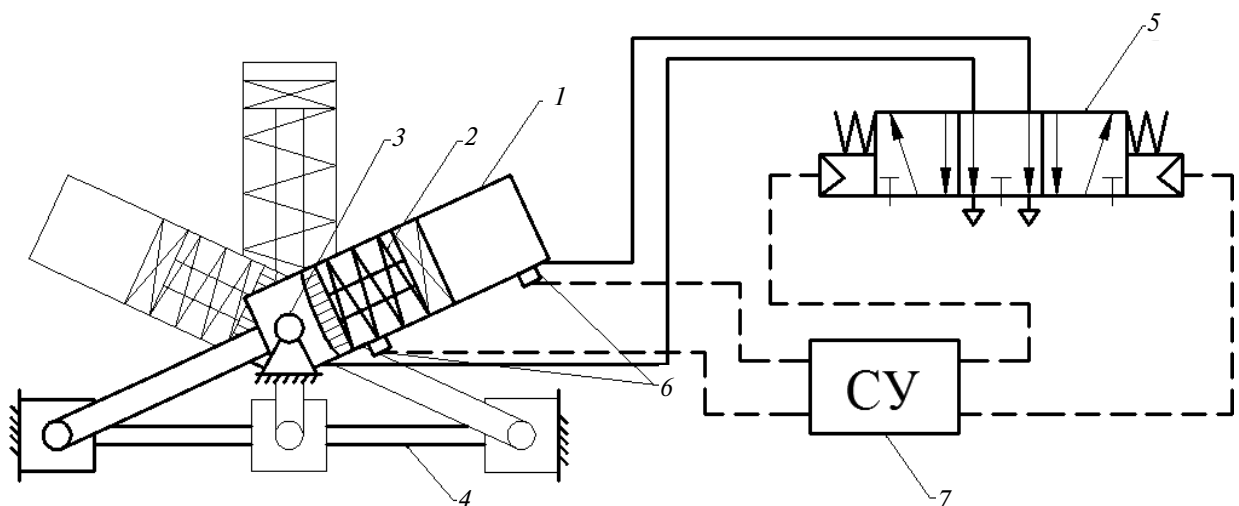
Пружинный привод механизма протягивания упаковочного материала:
